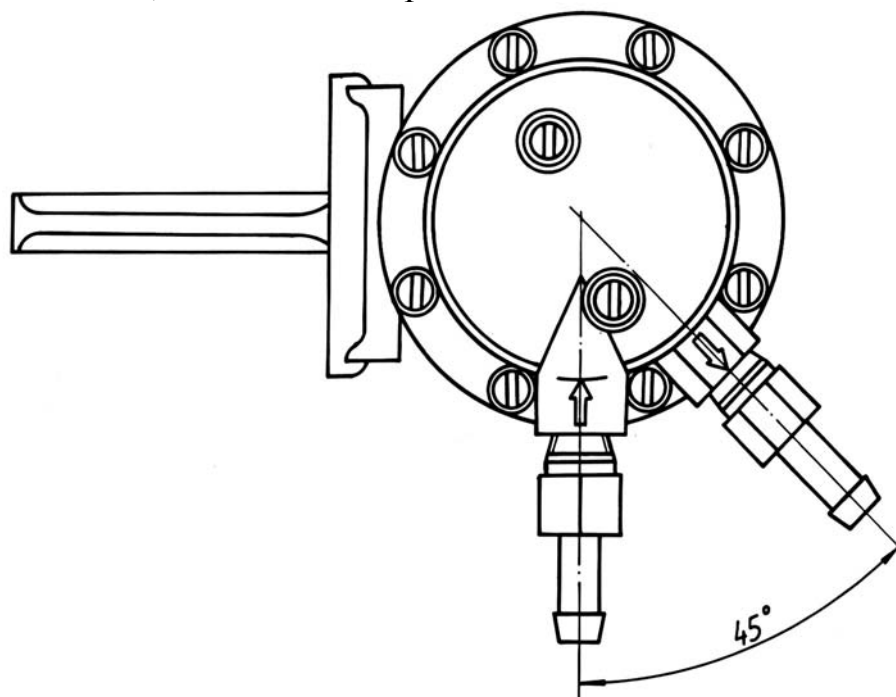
Положение головки и крышки топливного насоса относительно корпуса
